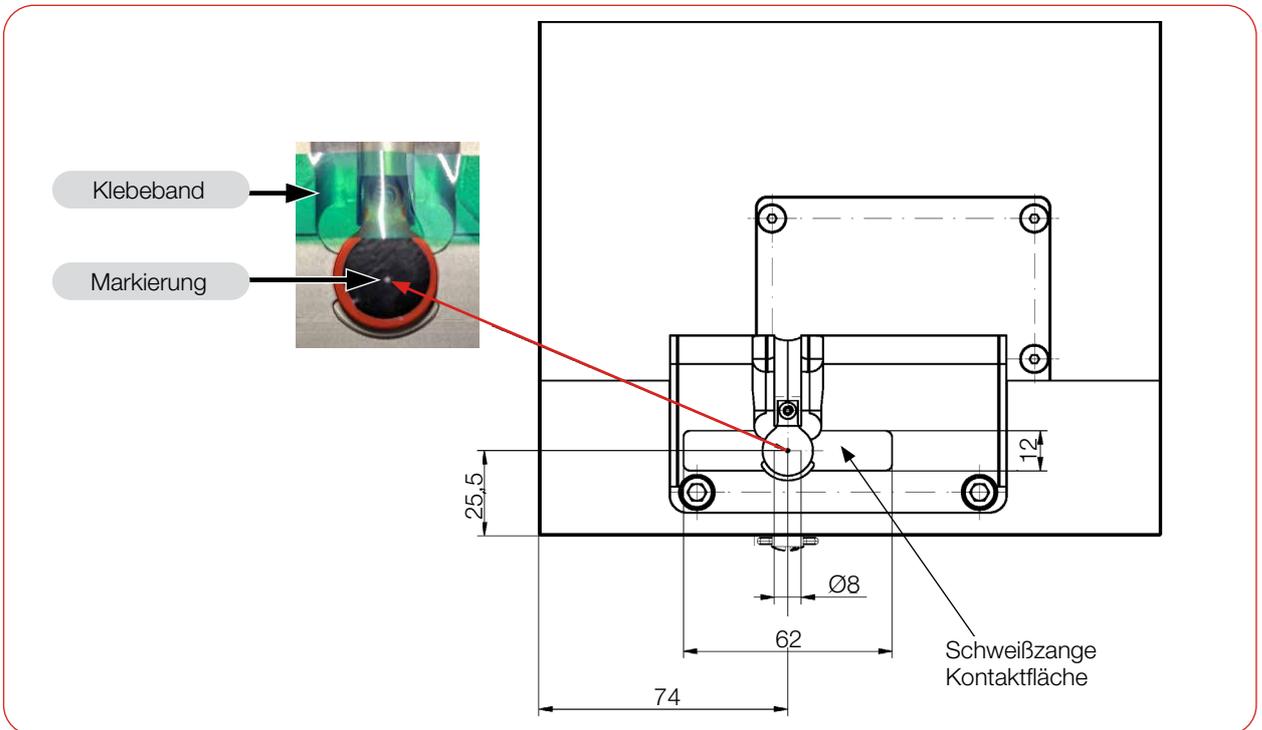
Ausrichtung des Gerätes zum Laserstrahl (Maße in mm)
